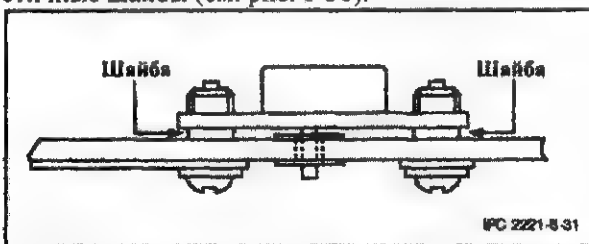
Металлический мощный корпус с эластичными шайбами
